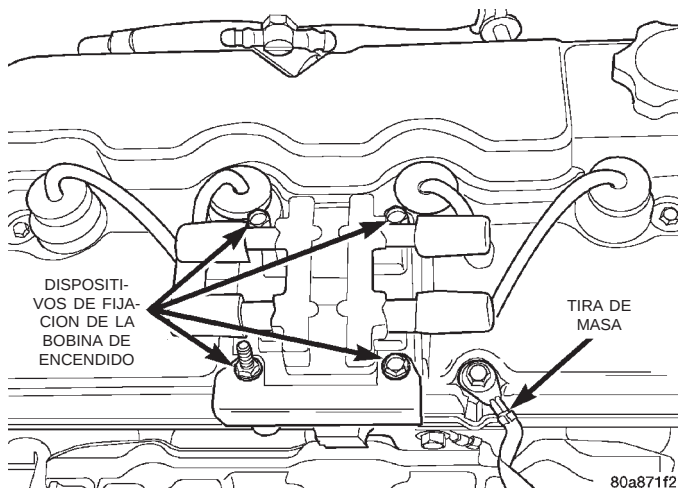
Conjunto de la bobina de encendido y tira de masa
